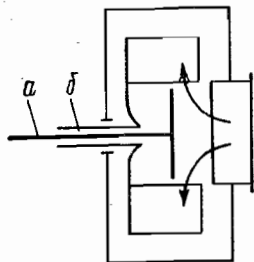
Схема регулировки вентилятора изменением активной ширины колеса: а — вал регулировочного диска; б — пустотелый вал колеса вентилятора
